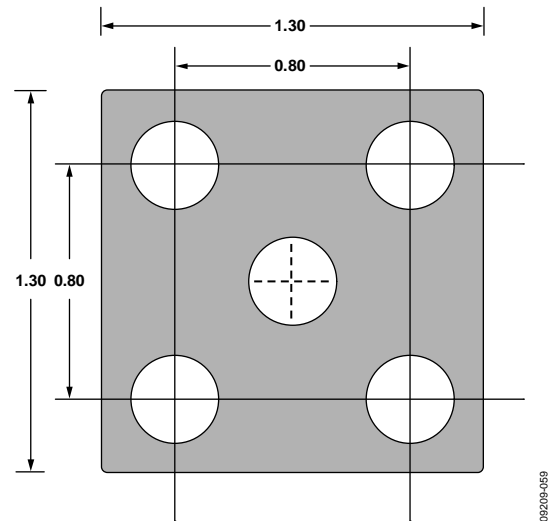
PCB サーマル・アタッチ・パッドの推奨寸法 (mm)
